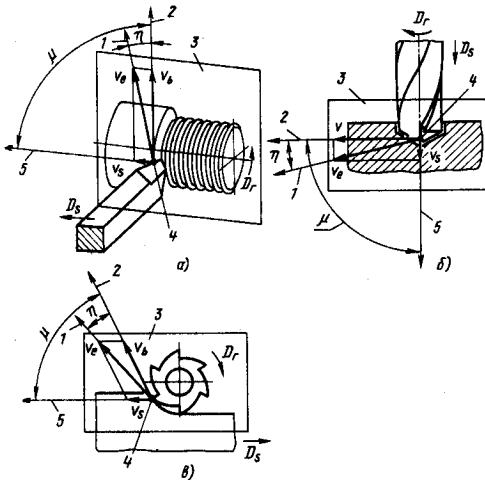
Элементы движений в процессе резания при обтачивании (а), сверлении (б) и фрезеровании (в): 1 — направление скорости результирующего движения резания; 2 — направление скорости главного движения резания; 3 — рабочая плоскость; 4 — рассматриваемая точка режущей кромки; 5 — направление скорости движения подачи
